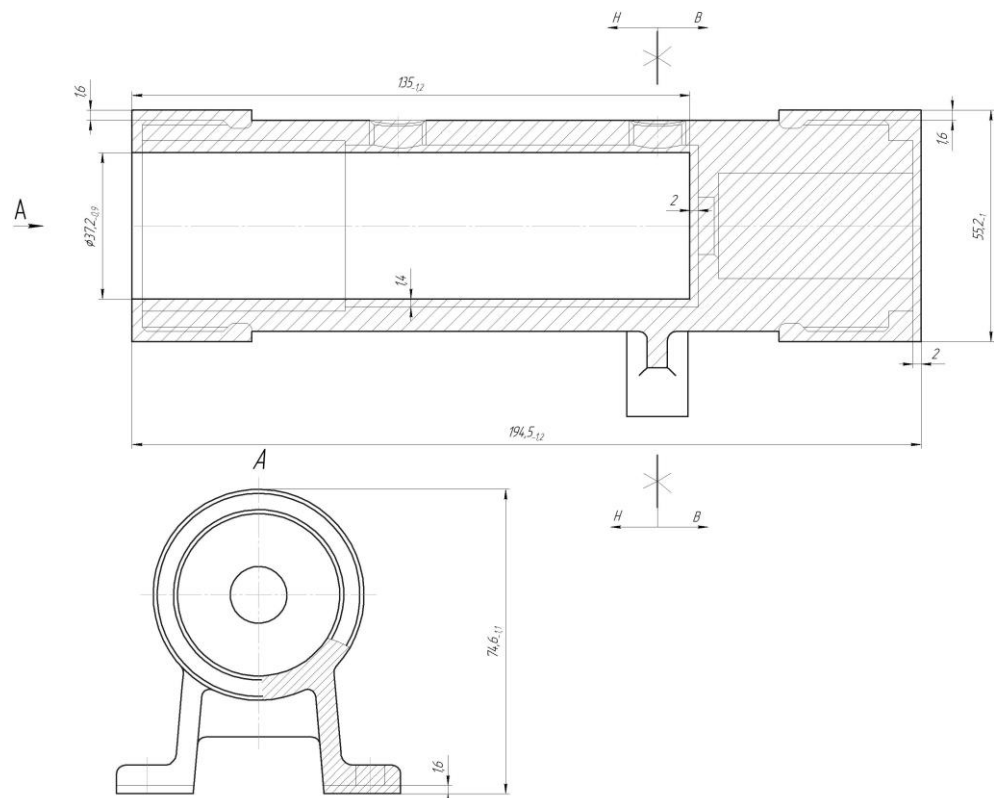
Ескіз заготовки з припусками отриманими литтям в піщані форми з машинною формовкою
